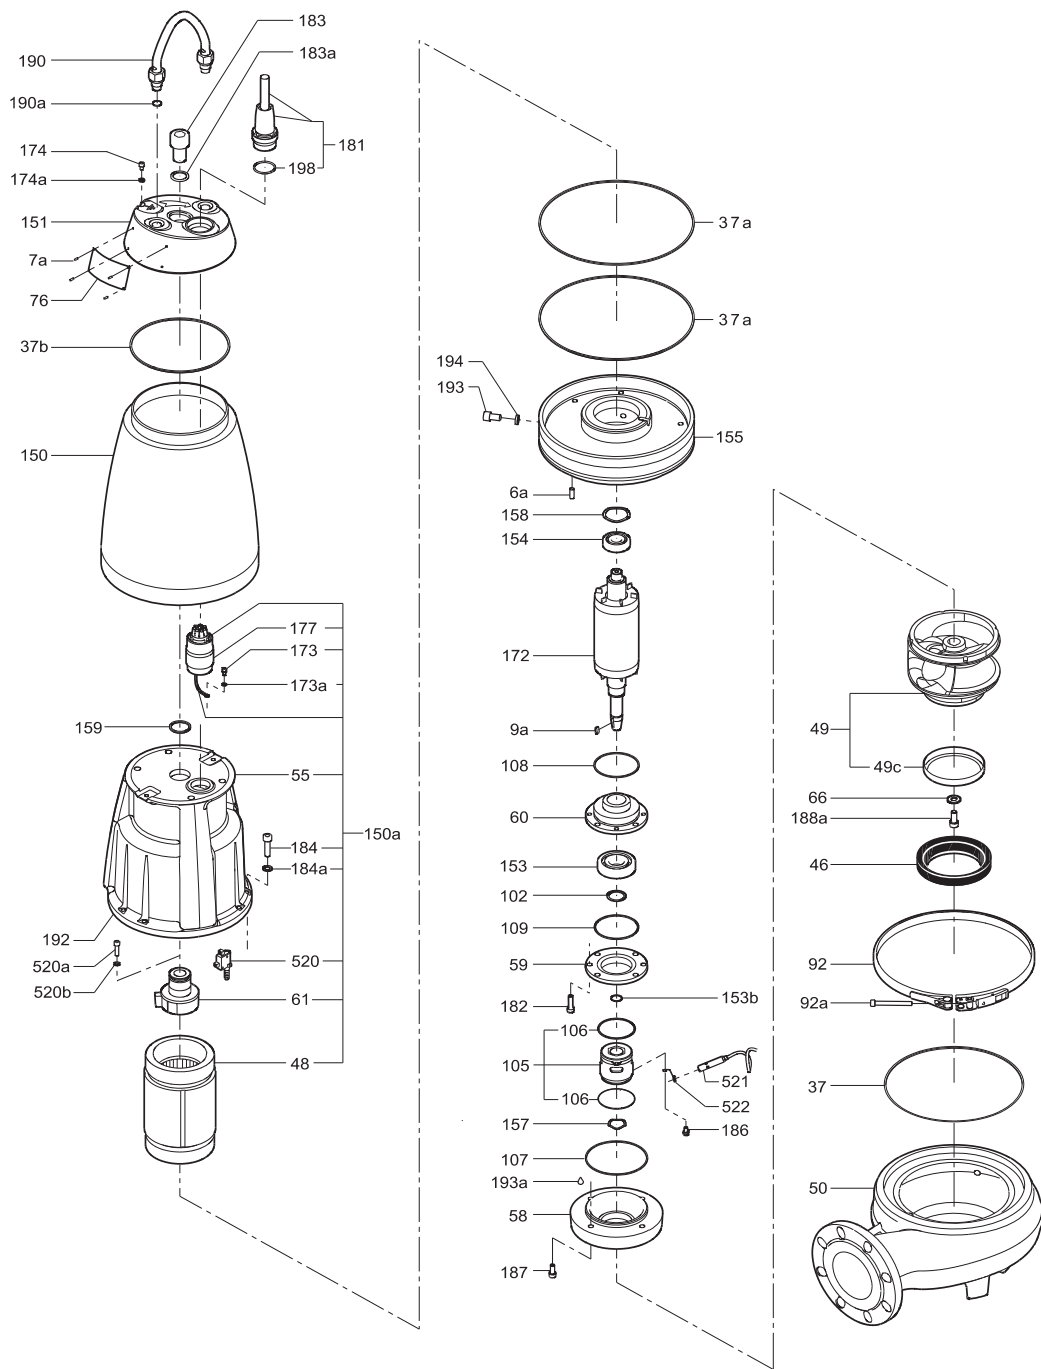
Детализовка насоса SE1 с одноканальным рабочим колесом S-tube (исполнение с датчиками)
